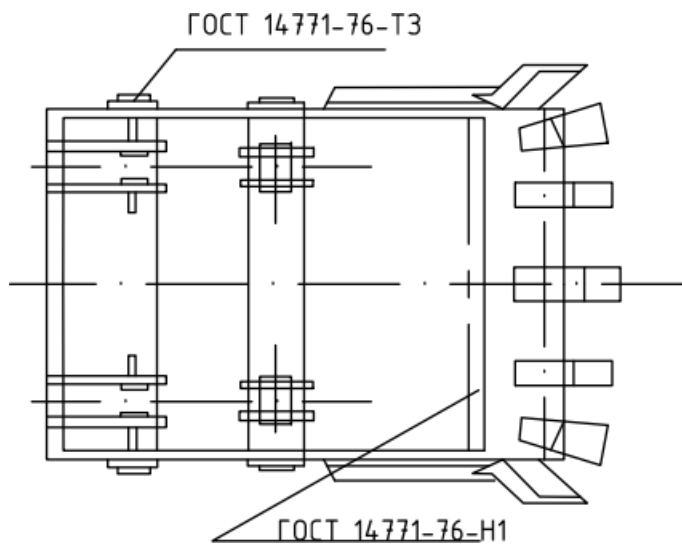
Складання і зварювання складальних одиниць ковша екскаватора.
